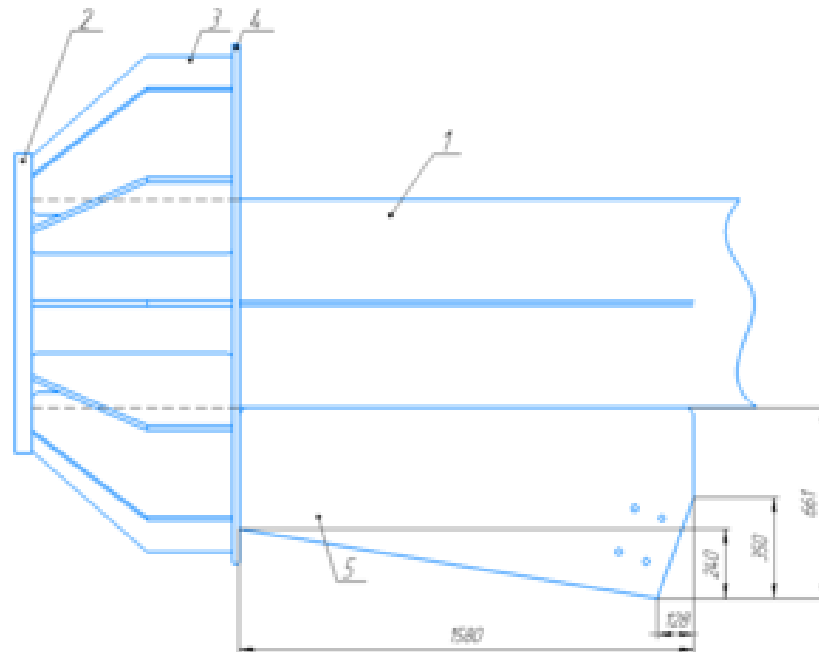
Сварка двух листов 5 профилем 661x12 с конструкцией
